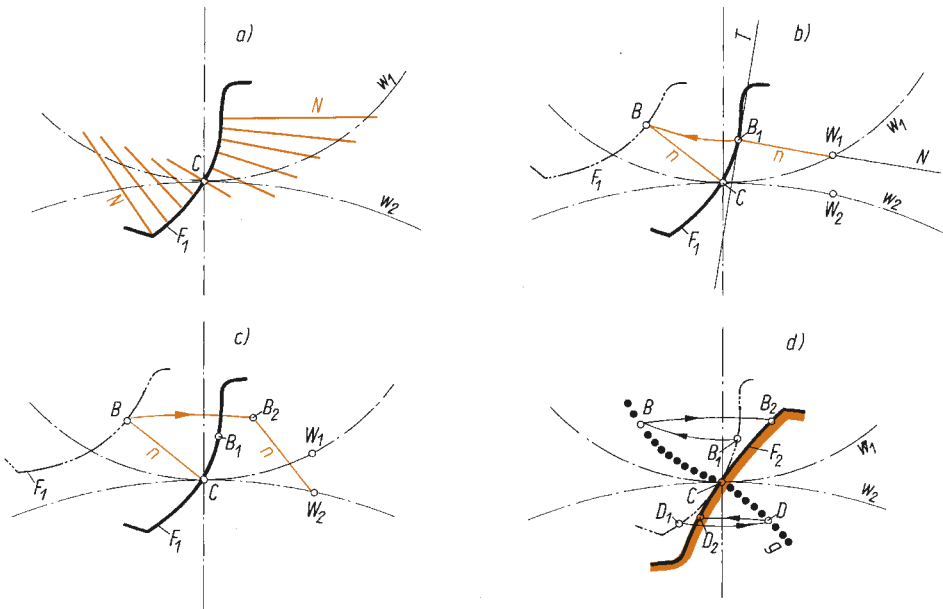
Ermitteln der Gegenflanke  $F_2$  zu einer gegebenen Flanke  $F_1$
